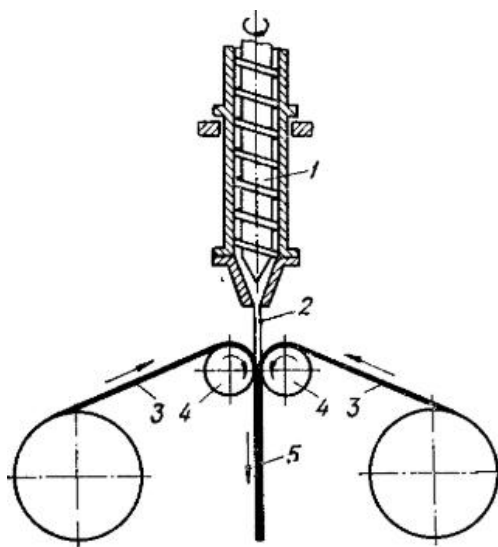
Схема сварки расплавом, получаемым экструзией
